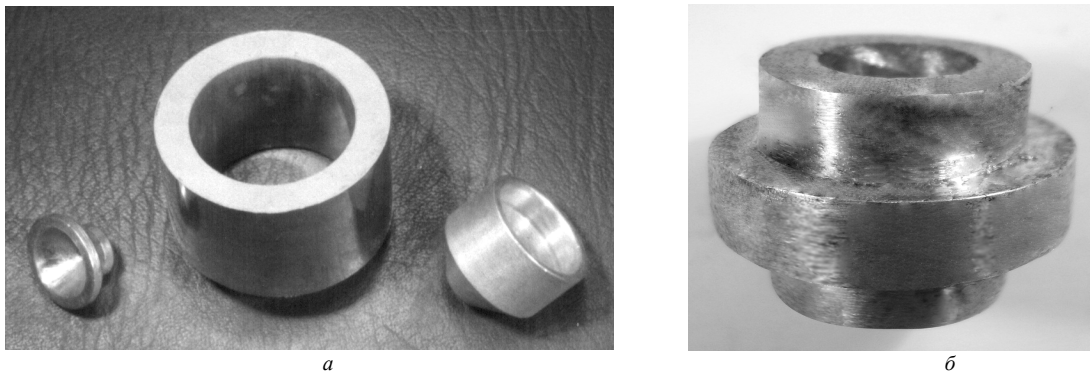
Деталі з мідного порошкового матеріалу: а - вкладиш підшипника ковзання, сопла плазмотрона; б - втулка з буртом
